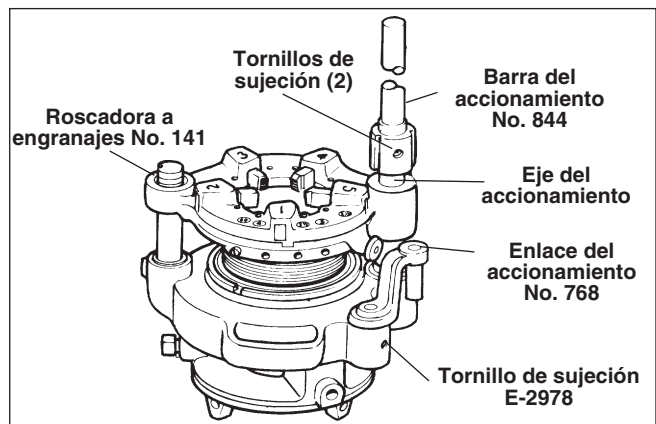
Roscadora a engranajes No. 141 con la Barra del accionamiento No. 844 instalada
